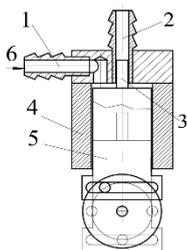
Схема устройства для прерывистой подачи сжатого воздуха
